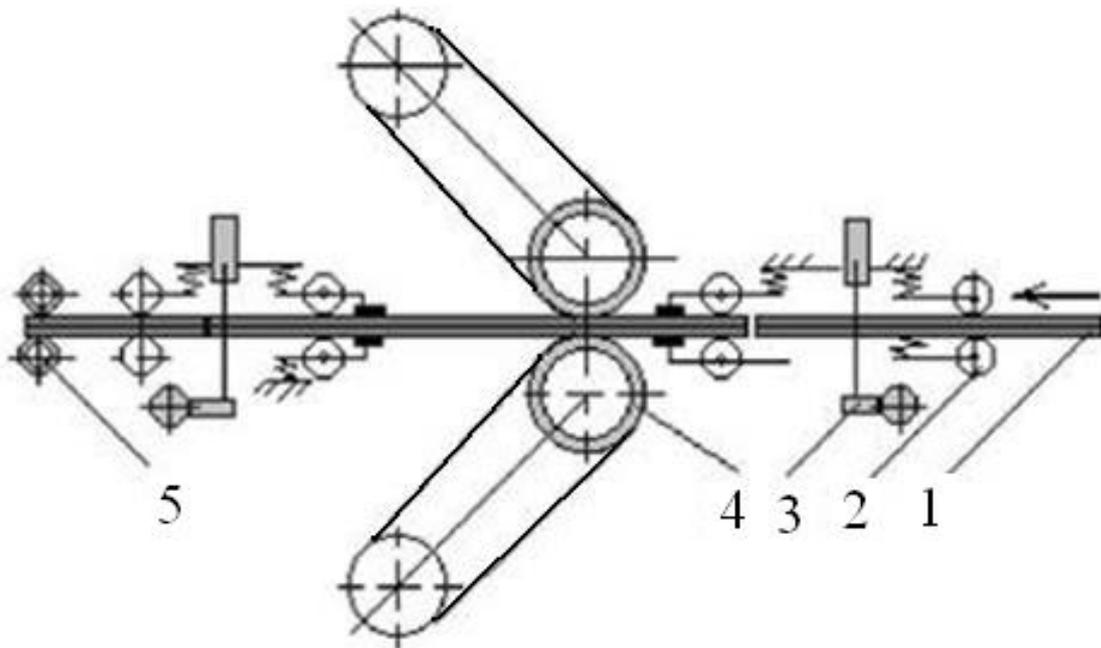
Схема широколенточного станка с контактными вальцами:
